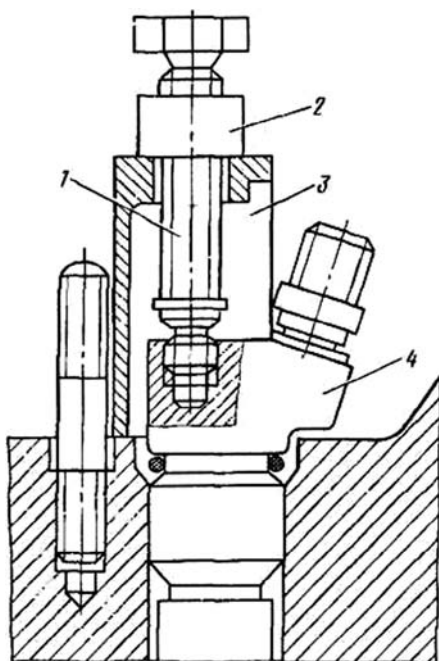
Снятие форсунки с двигателя съемником 740.3901210: 1 — винт; 2 — гайка; 3 — стойка; 4 — форсунка
